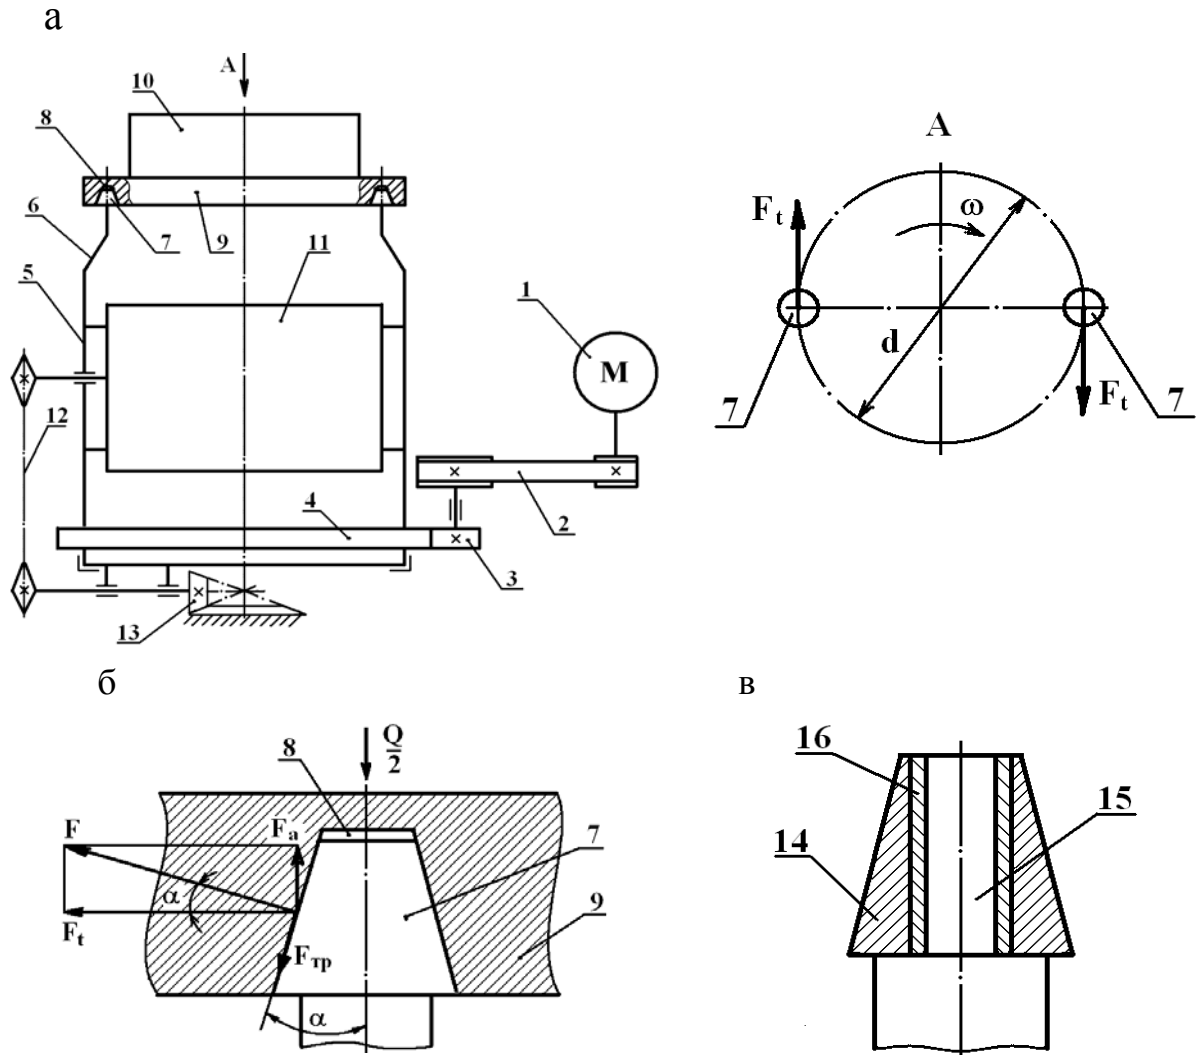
Привід круглов'язальної машини: а - кінематична схема приводу; б - схема сил, що діють на палець водила; в - схема робочої частини пальця
